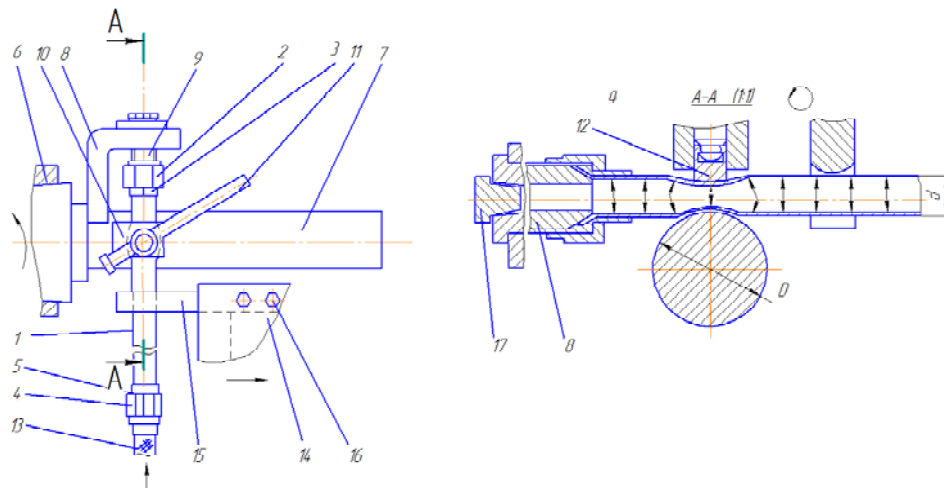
Початкове положення трубної заготовки перед гнуттям з підпором
